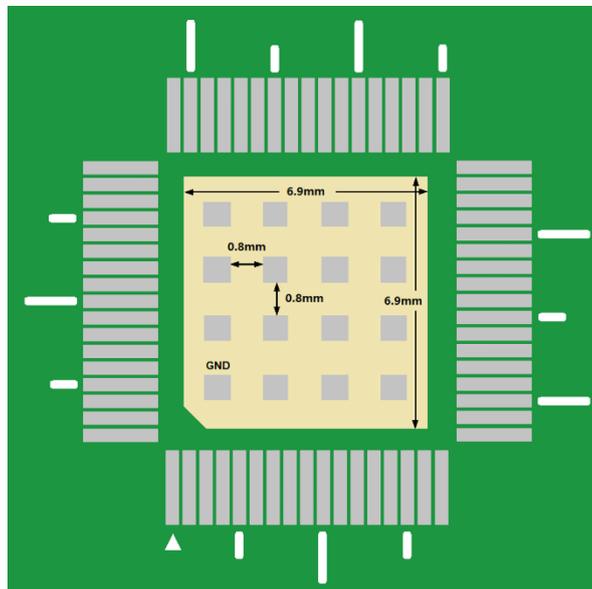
LT7580 (QFN80) 焊盘与脚位图
